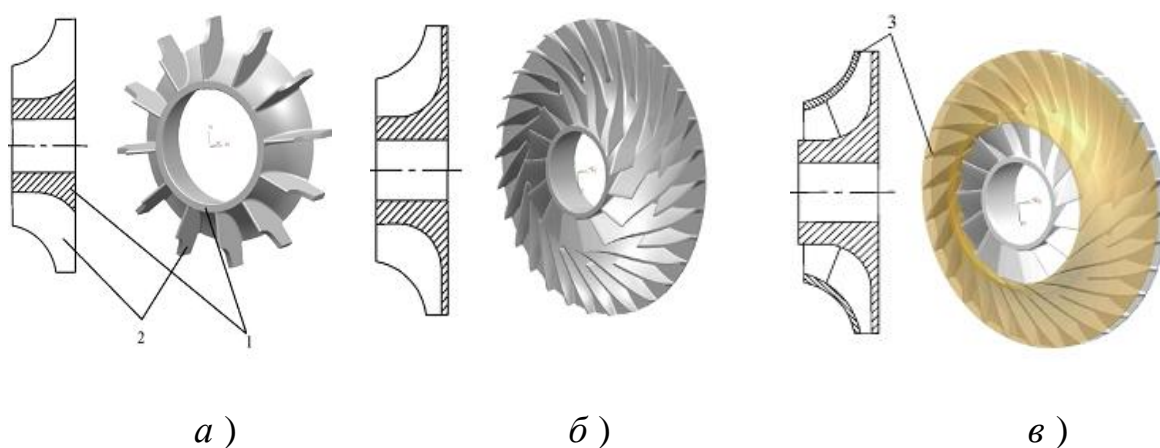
Схемы рабочих колес центробежного компрессора
